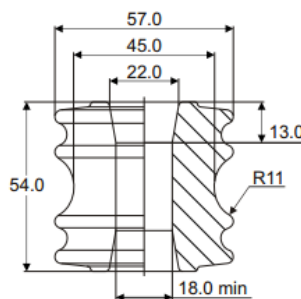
Dimensiones aislador tipo carrete ANSI 53-1.
